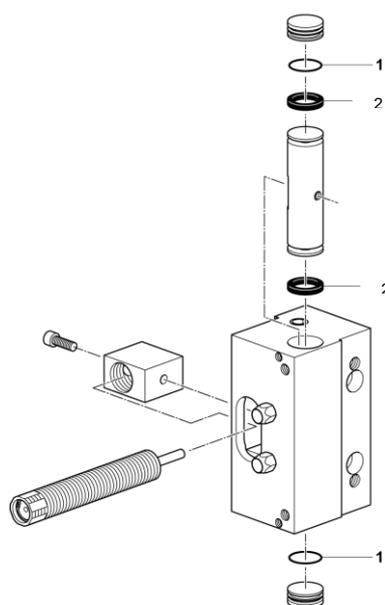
Pièces de rechange pour ZA 32 - comprises dans le kit
